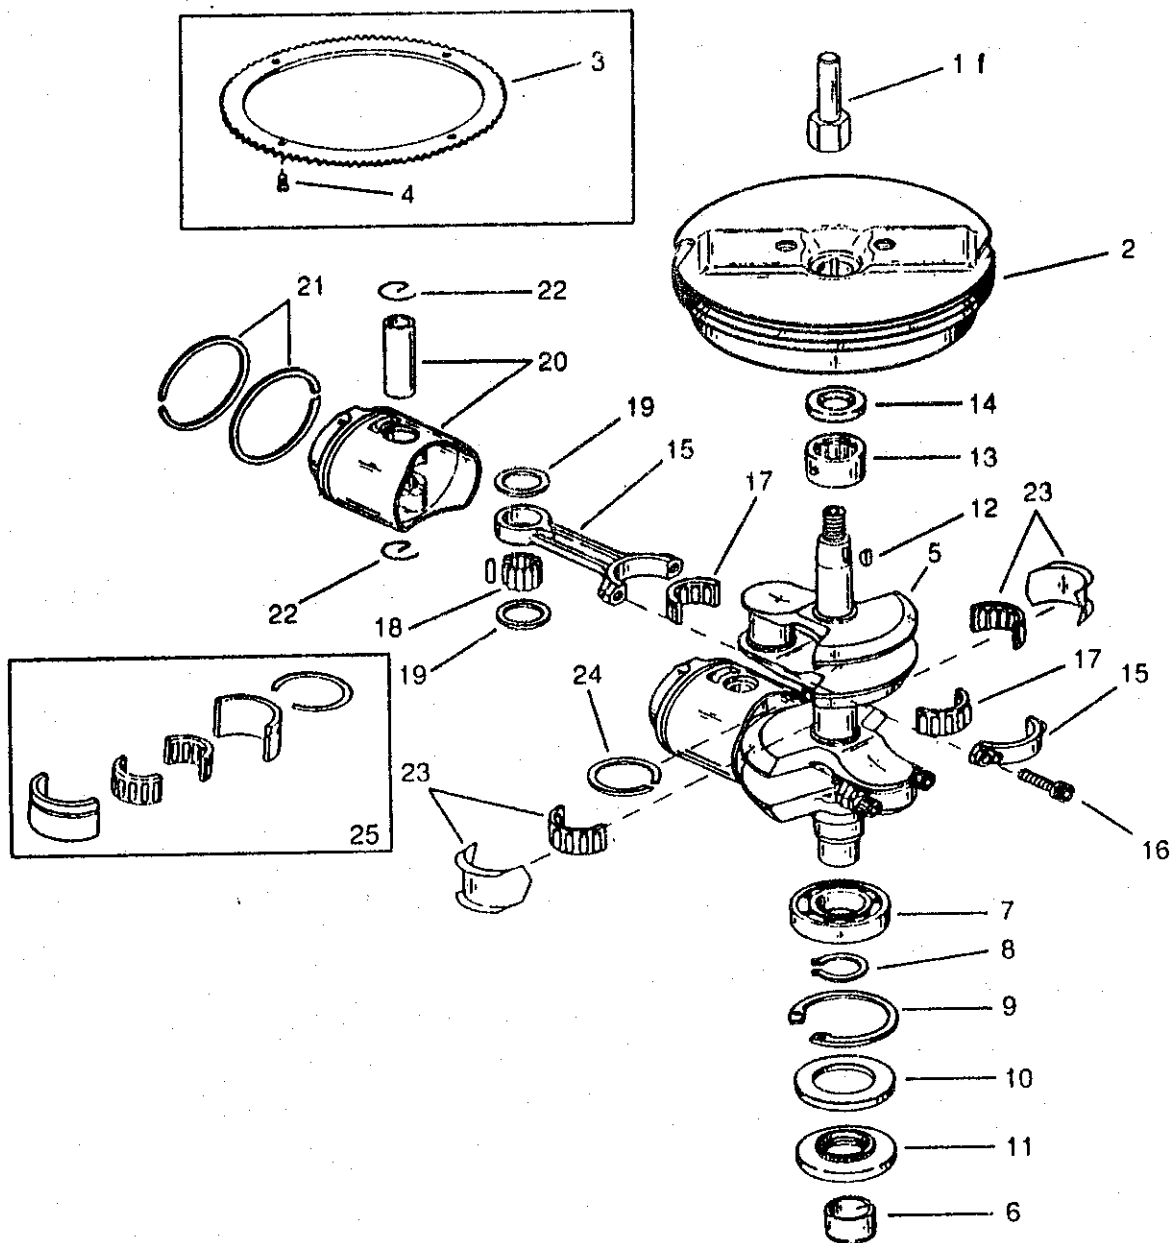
Componentes del eje cigüeñal, motor de 2 cilindros.
